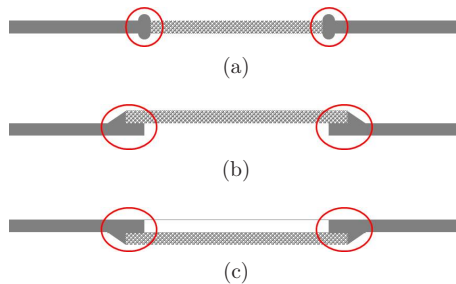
Einschweißkonzepte von metallgetragenen Gasmodulen.
